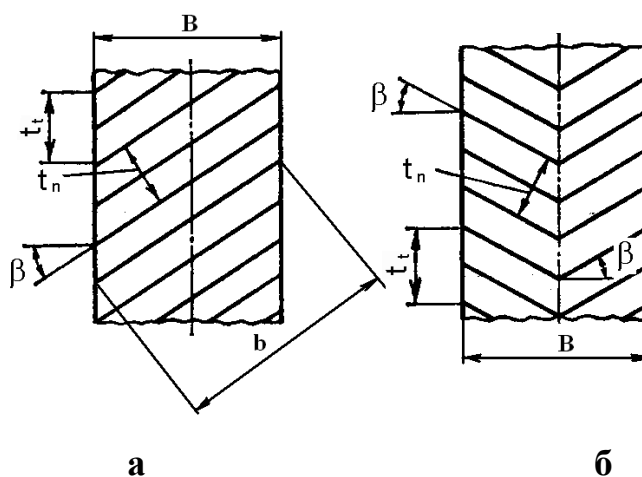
Схеми циліндричних зубчастих коліс: а – косозубого; б – шевронного
